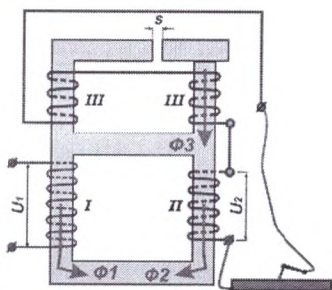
Схема сварочного трансформатора типа СТН
